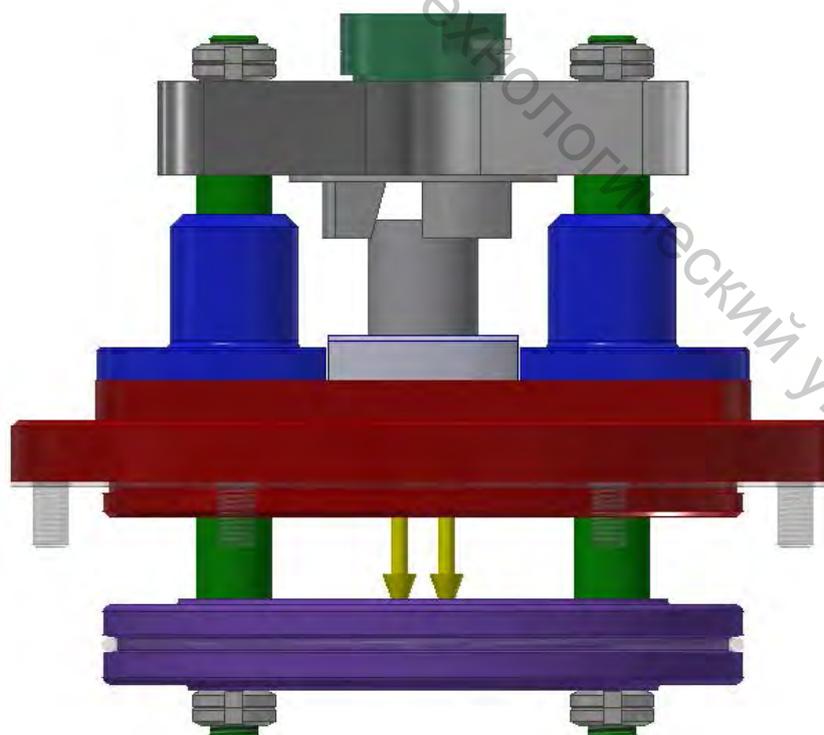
Кондуктор для зенкерования отверстий.
